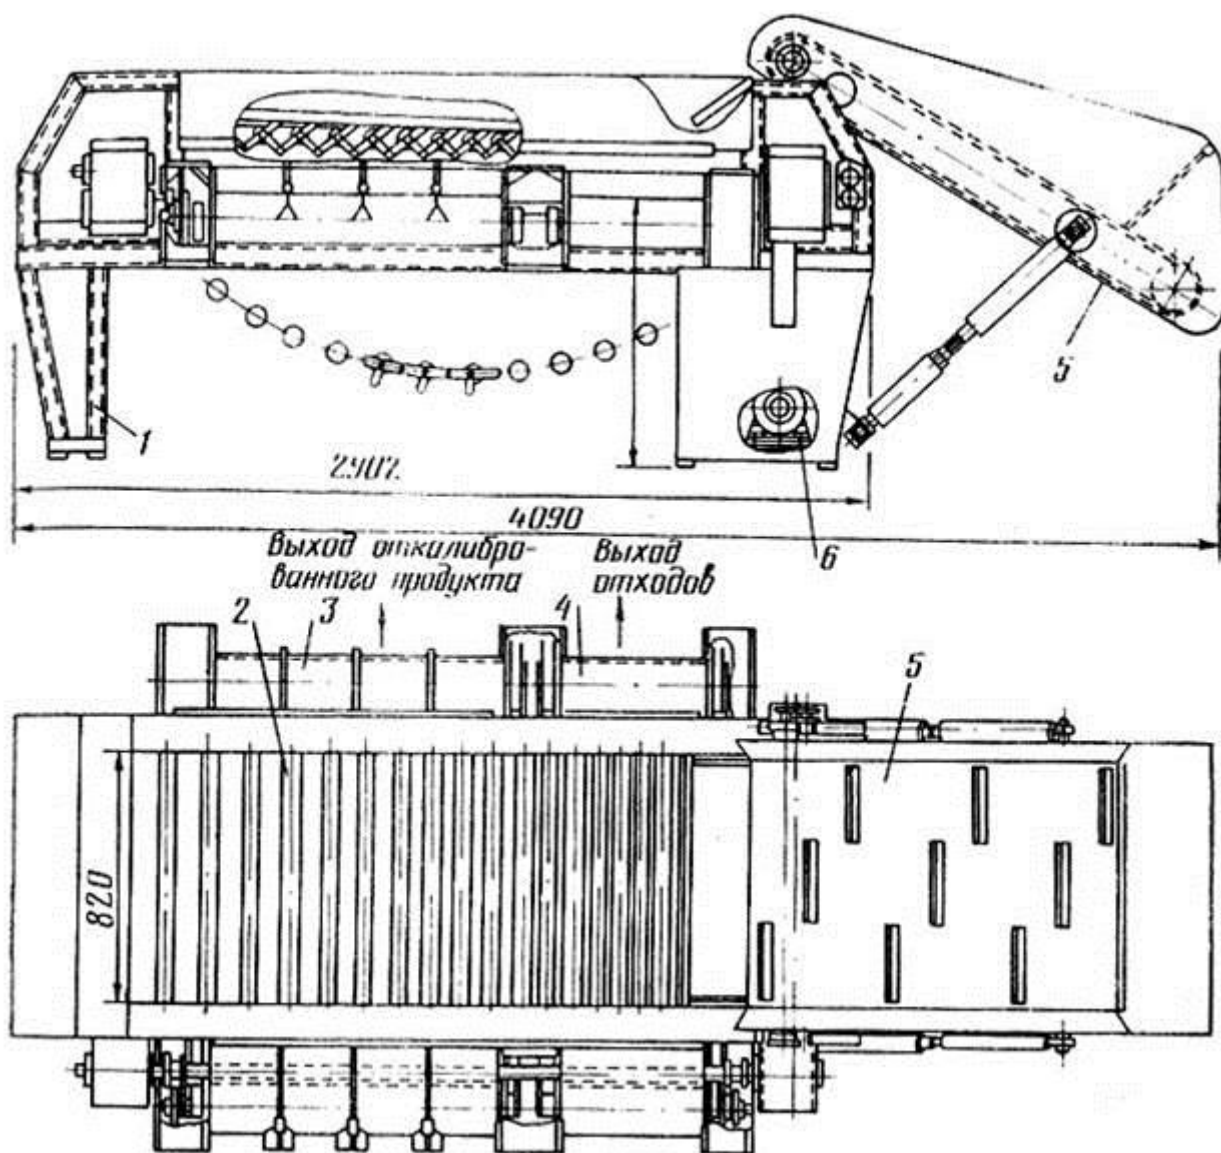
Калиброватель универсальный А9-ККБ: 1 - станина; 2 - ролики; 3 - фракционный транспортер; 4 - транспортер отходов; 5 - элеватор; 6 - электродвигатель
